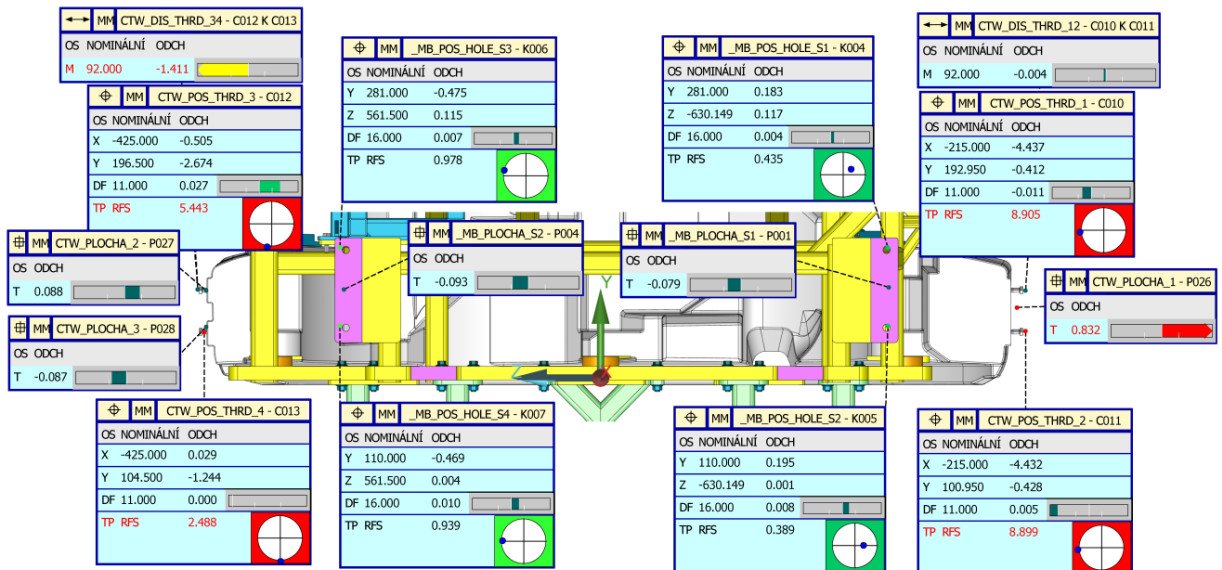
Rozměrová kontrola přípravku 1/6
